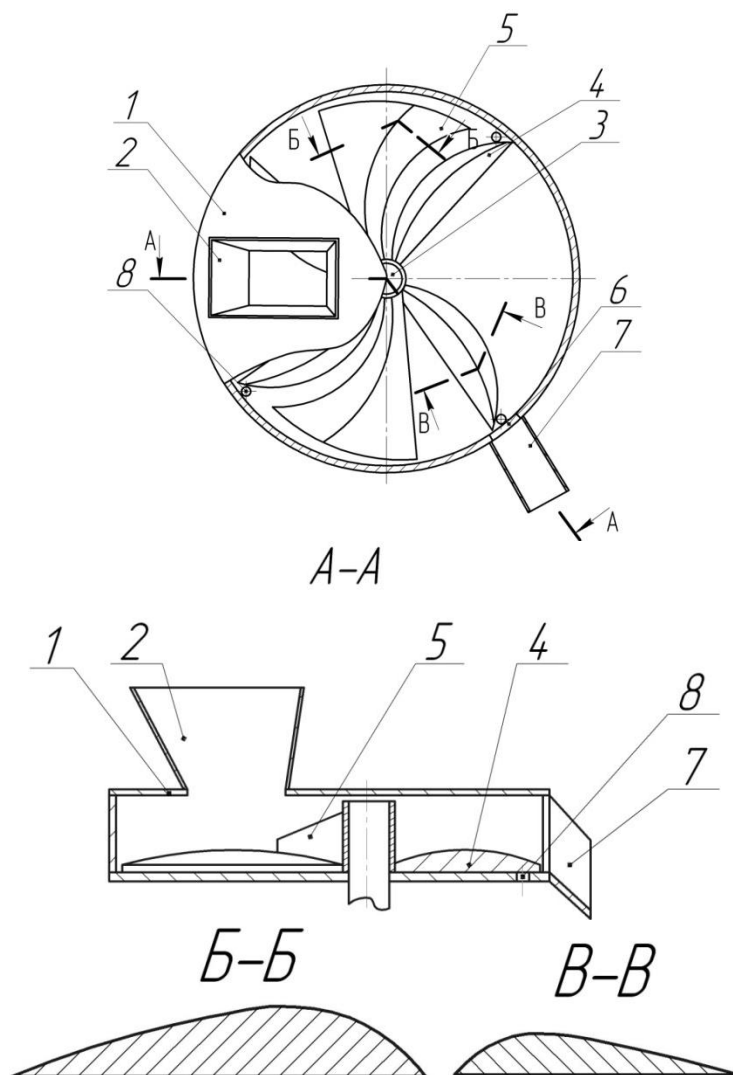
Конструктивно-технологическая схема устройства для отжима влаги:
